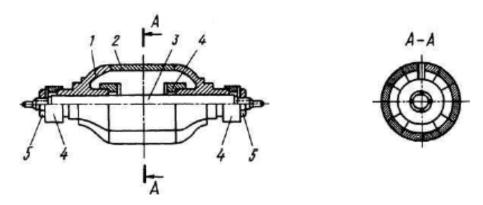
Конструктивная схема металлической оправки: 1 - разборные части оправки, формирующие днища сосудов; 2 - цилиндрическая часть оправки; 3 - вал; 4 - гайки для сборки частей днищ; 5 - гайки крепления оправки на валу
